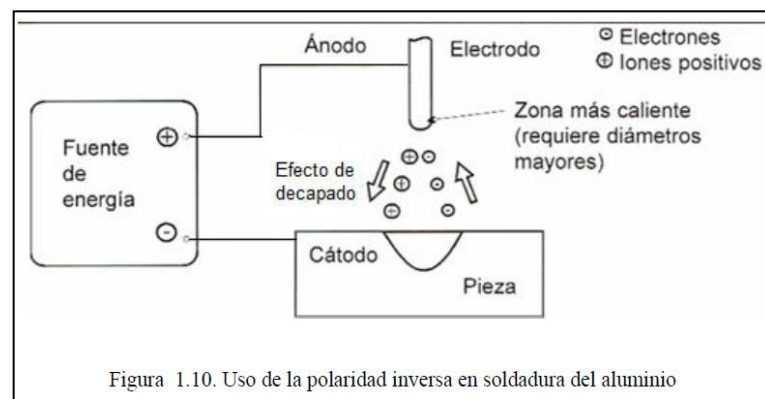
Uso de la polaridad inversa en soldadura del aluminio
